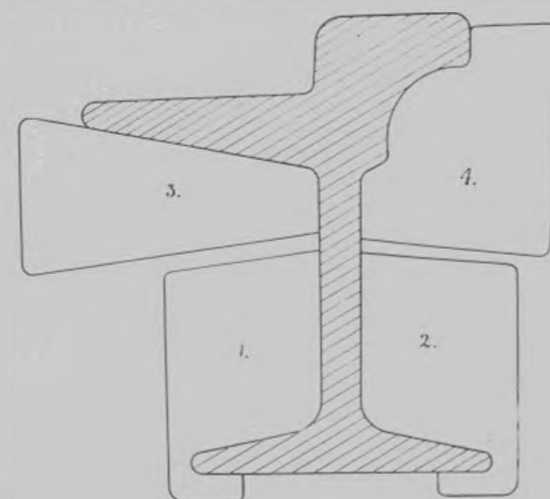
DISPOSITION DES PIÈCES POUR SOUDER LES RAILS
